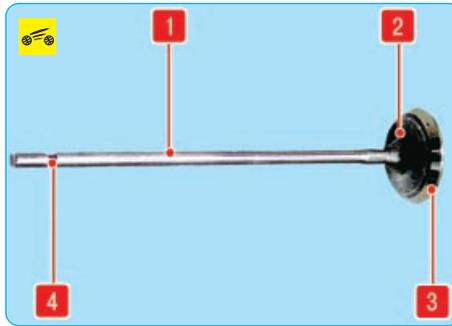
Клапан: 1 – стержень; 2 – тарелка; 3 – фаска; 4 – проточка
